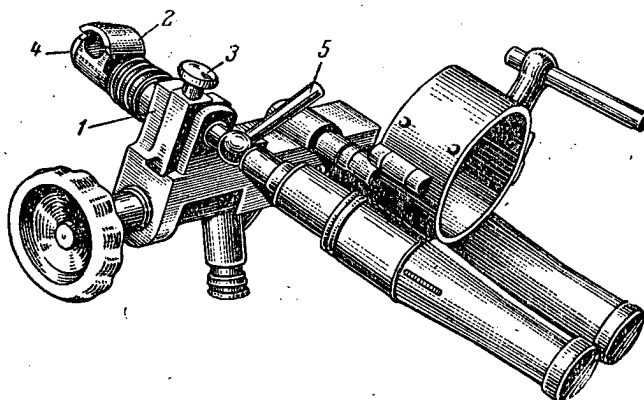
Вертлюг с качающимся кронштейном: 1—корпус; 2—хомут; 3—винт; 4—фиксатор; 5—рукоятка
